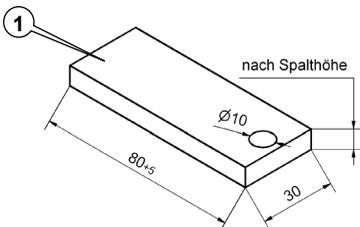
Flachstahl für Oberzargenbefestigung (Maßskizze)
